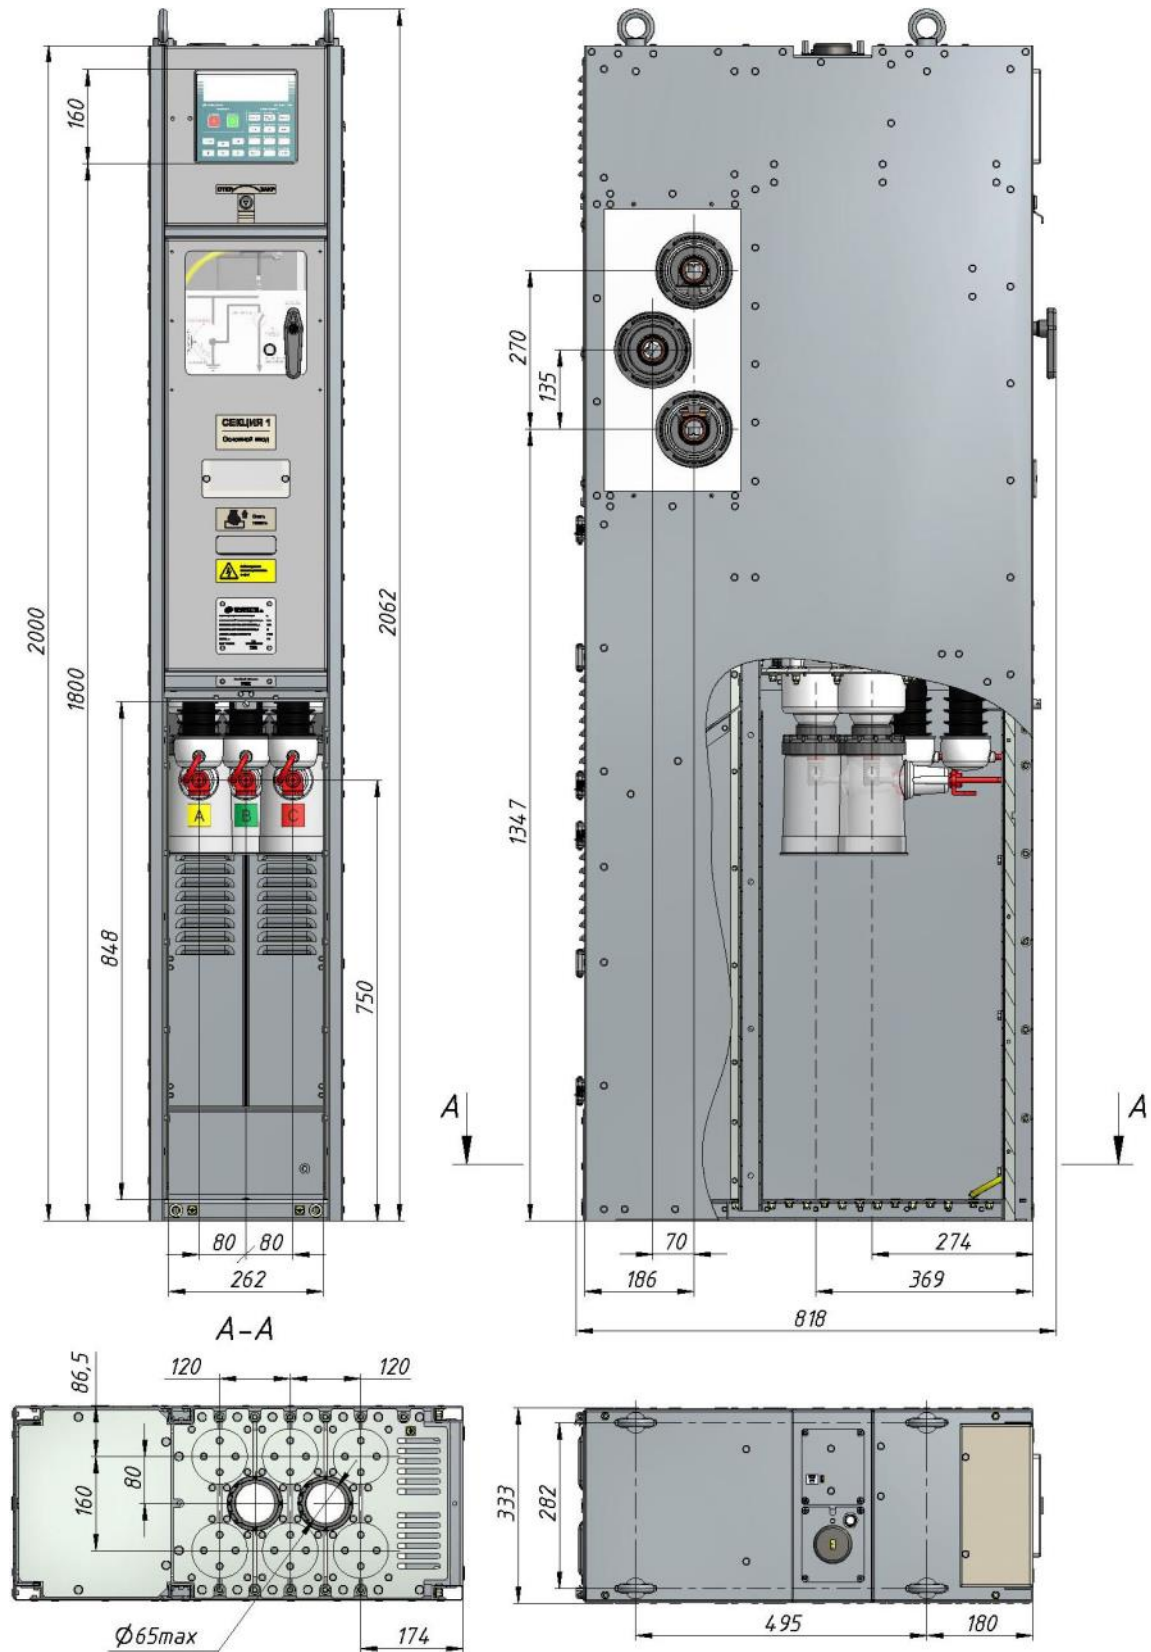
Габаритный чертеж TER_SP15_Etalon_1
